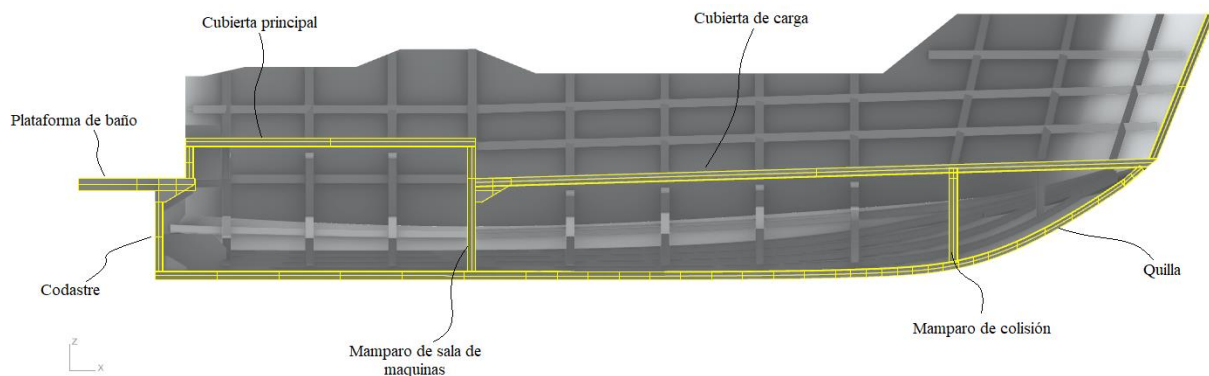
Vista longitudinal de los principales elementos estructurales de la embarcación.
